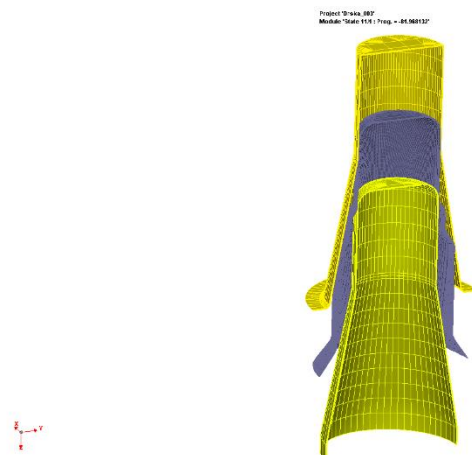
Zobrazení sítě a uložení sestavy v 4 OP
